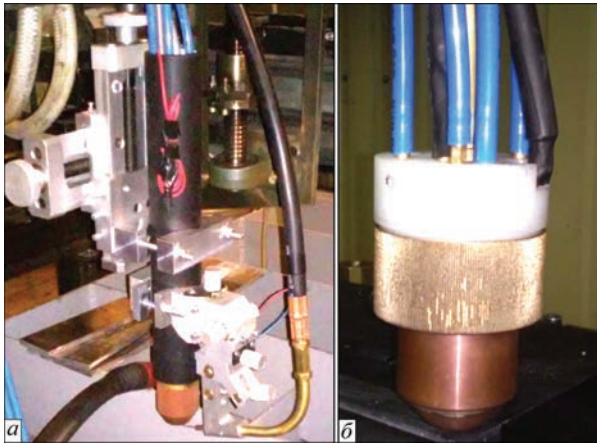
Плазмотроны разработки ИЭС им. Е. О. Патона для плазменно-дуговой сварки неплавящимся (а) и гибридной плазменно-дуговой сварки плавящимся (б) электродами
